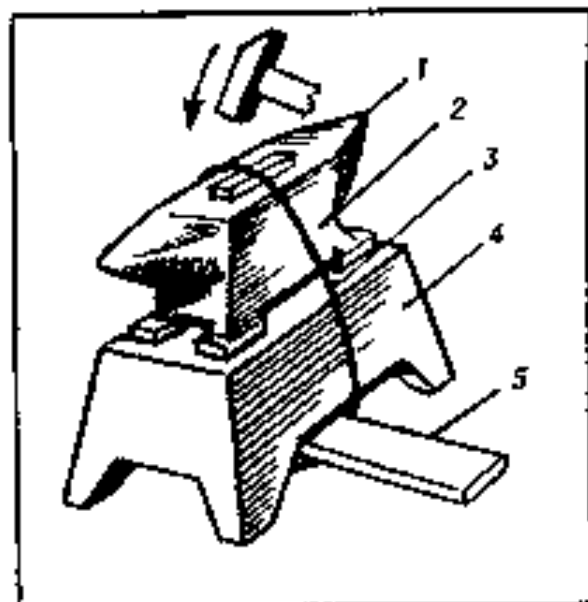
Удерживание заготовки на наковальне с помощью петли из троса:
